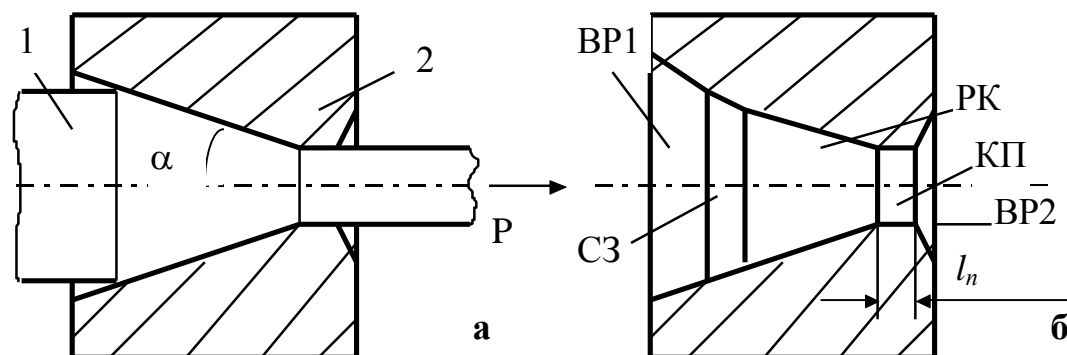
Схема волочения прутка или проволоки(а): 1- заготовка; 2 - волокна(фильера) и продольное сечение волокна(б): ВР1-входная распушка; СЗ-смазочная зона; РК-рабочий конус; КП-калибрующий пояс; ВР2-выходная распушка
